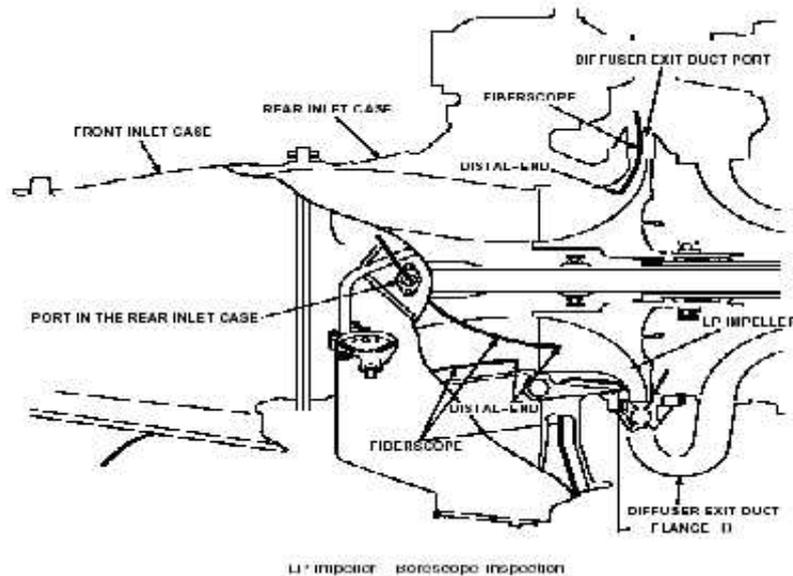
Inspection boroscopique du compresseur BP.
